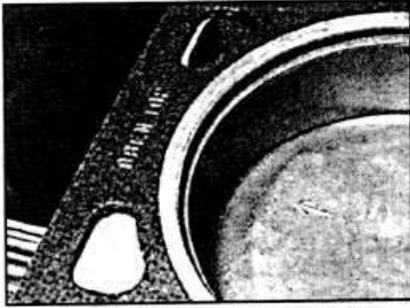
В.39. Установка прокладки головки блока цилиндров надписью "OBEN/TOP" вверх.
